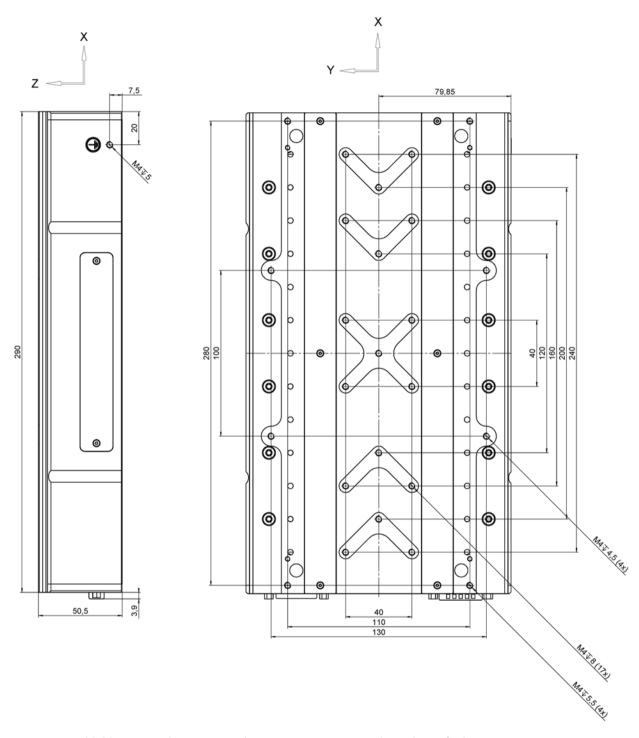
Abmessungen des V-551.4D: Seitenansicht und Draufsicht
